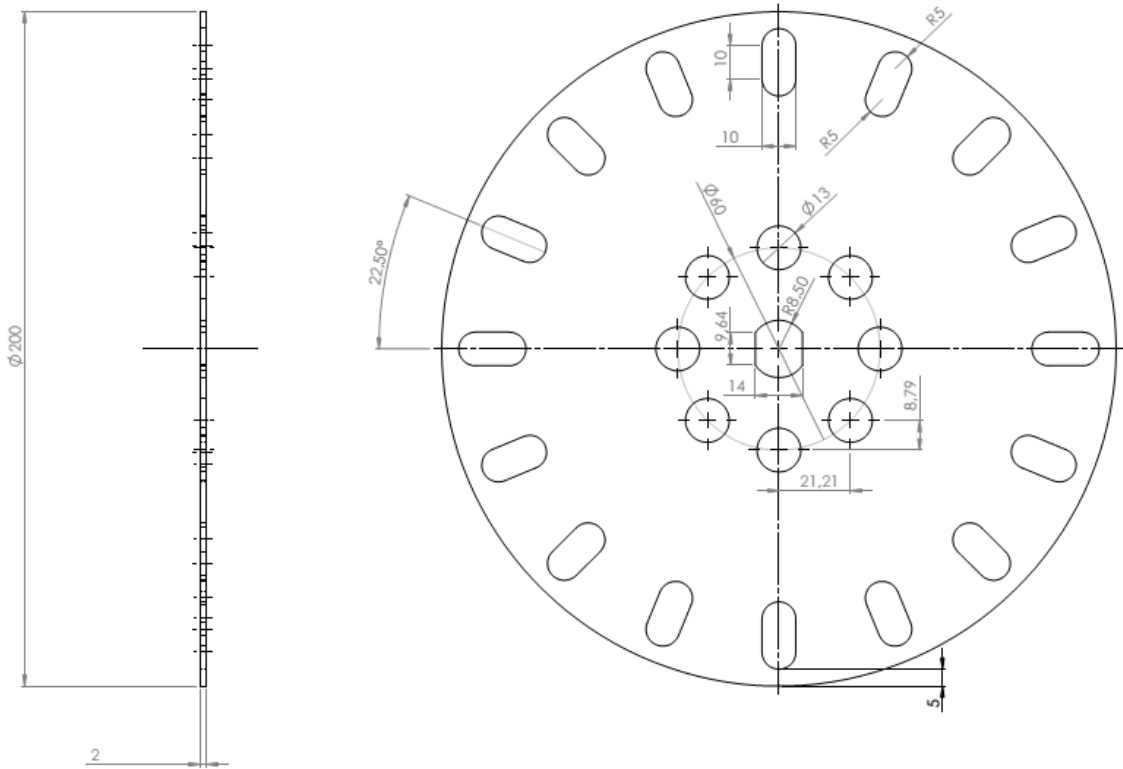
Dimensões (em milímetros) dos discos do rotor tipo E.
